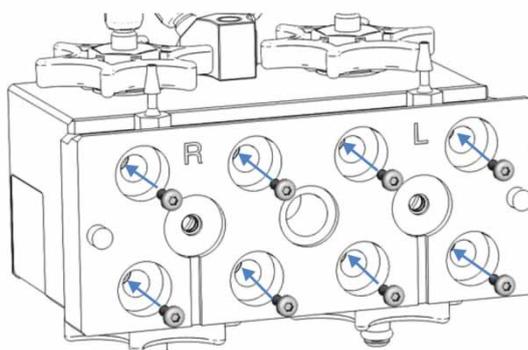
Pumpenkopf mit Hinterspülplatte und Schrauben für die Platte
